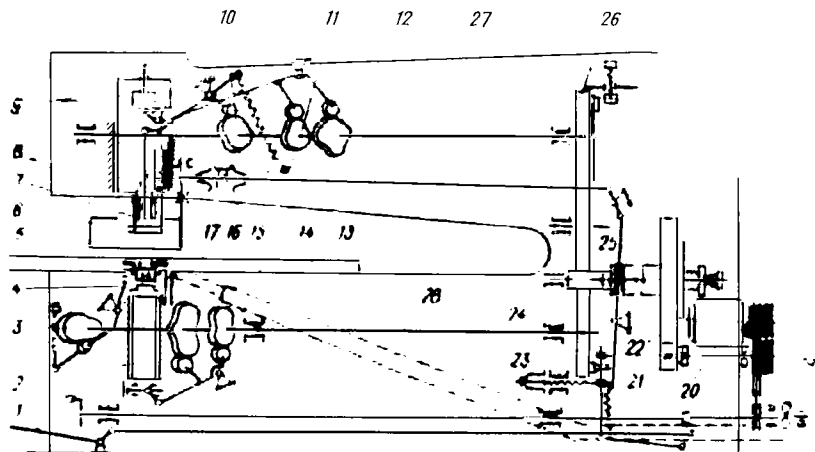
Кинематическая схема шпонопочиночного станка ПШ
